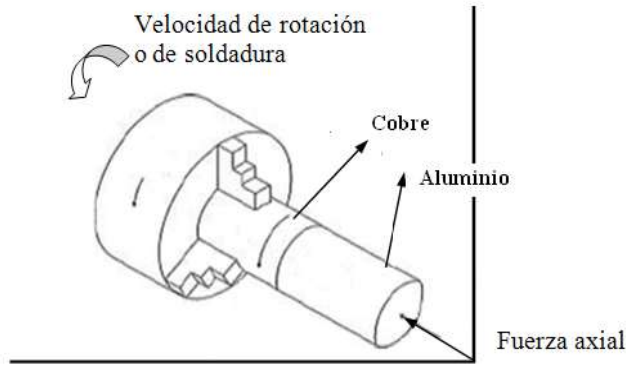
Modelo empleado para la soldadura por fricción radial o rotativa.
